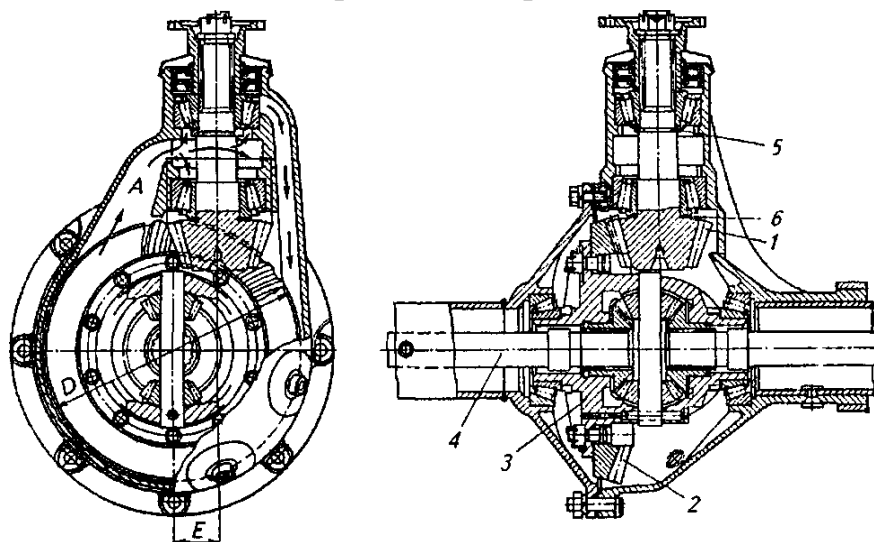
Гипоидная главная передача: 1 — шестерня; 2 — колесо; 3 — дифференциал; 4 — полуось; 5— регулировочная втулка; 6 - прокладки; Е— гипоидное смещение.
